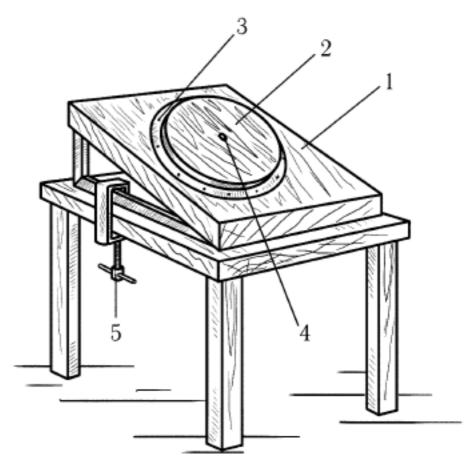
Настольная верстачная доска: 1 — наклонный деревянный щит; 2 — поворачивающийся круг; 3 — отверстия для шпилек; 4 — штырь; 5 — струбцина
